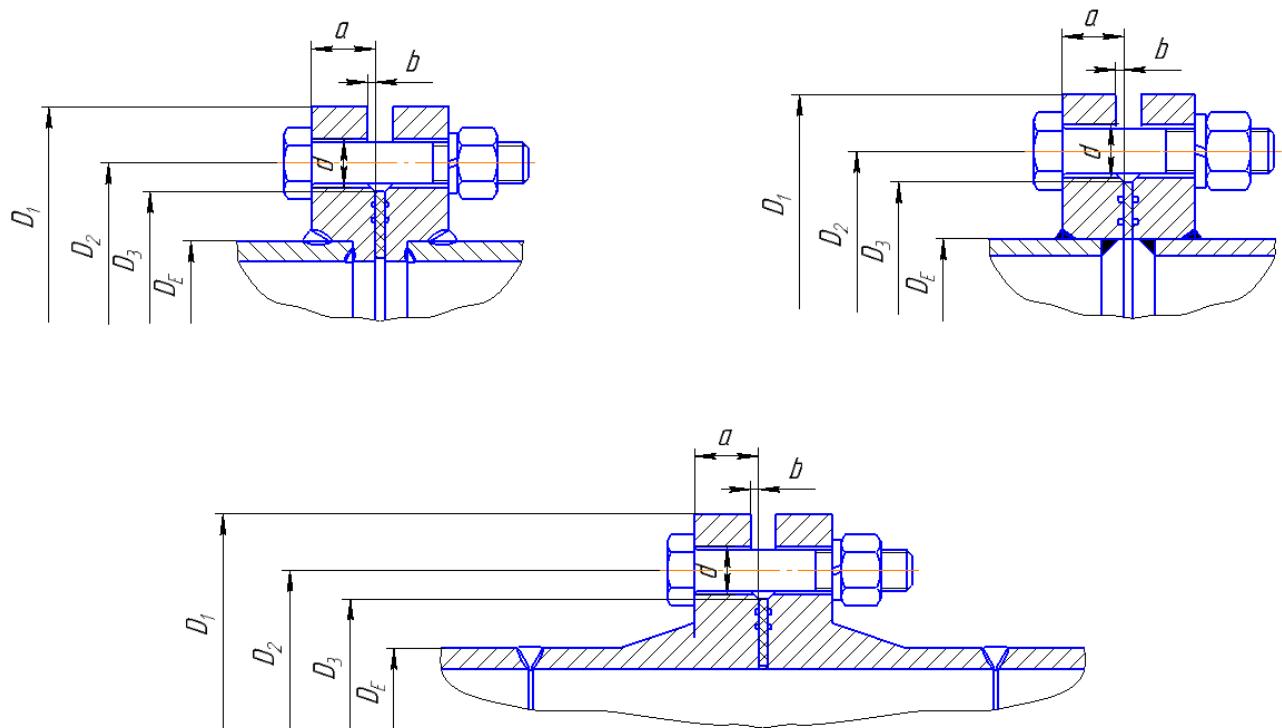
Варианты исполнения фланцевых соединений при изготовлении сварных фасонных частей
